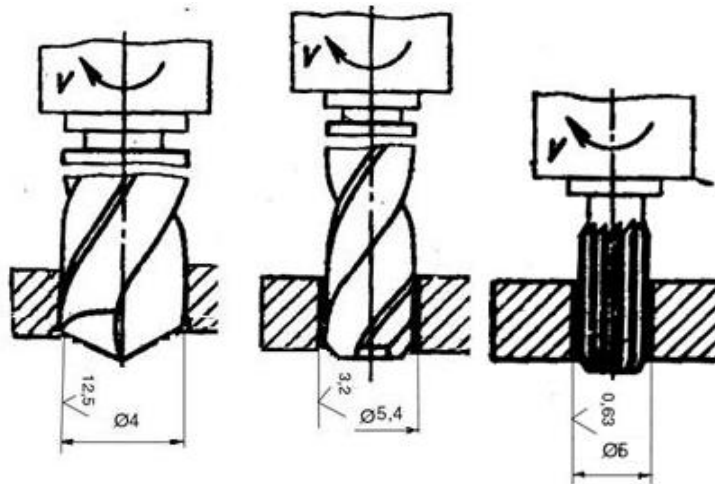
Чистова обробка отвору на вертикально-свердлильному верстаті
